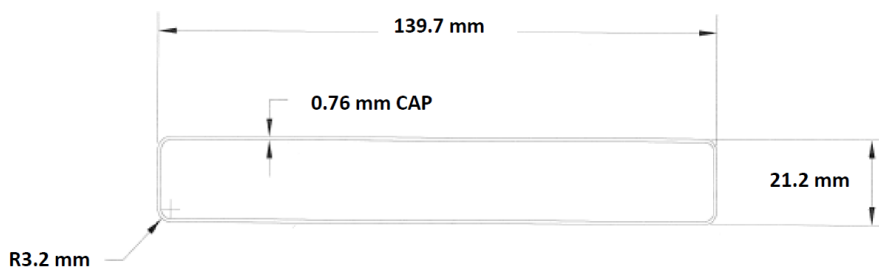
Profil plein des planches « DecKorators® Vault », « DecKorators® Voyage » et « DecKorators® Frontier »
